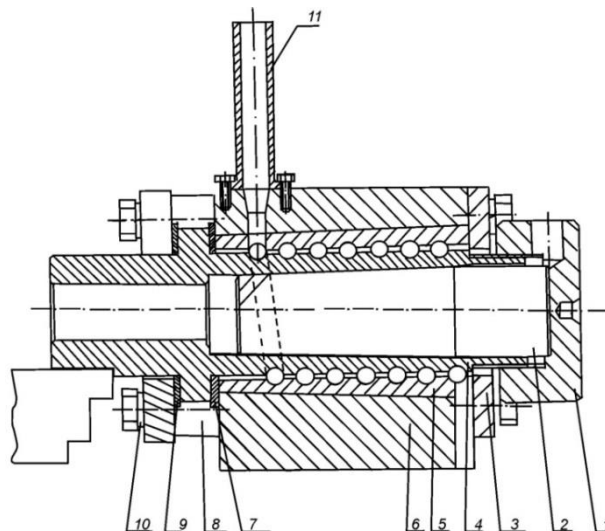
Инструмент для обкатки сферических заготовок (1- гайка прижимная, 2 – оправка, 3- крышка, 4 – шнек, 5 – вставка, 6 – корпус, 7 – шайба, 8 – втулка, 9 – шайба, 10 – крышка, 11 – накопитель шариков).
